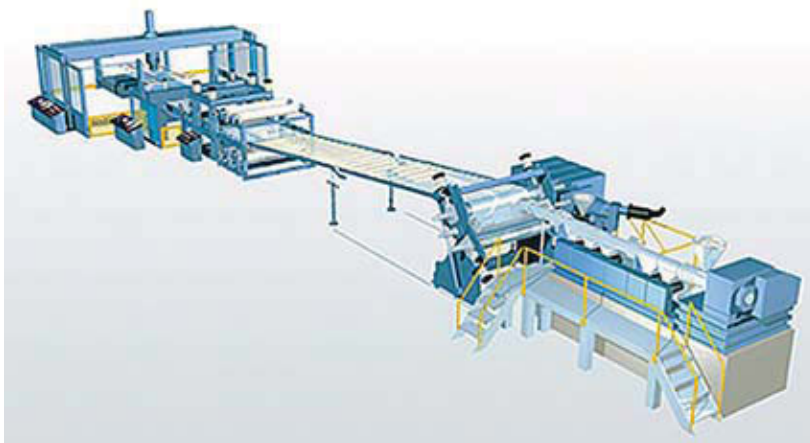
3D-Ansicht einer Tafelextrusionsanlage [9]
